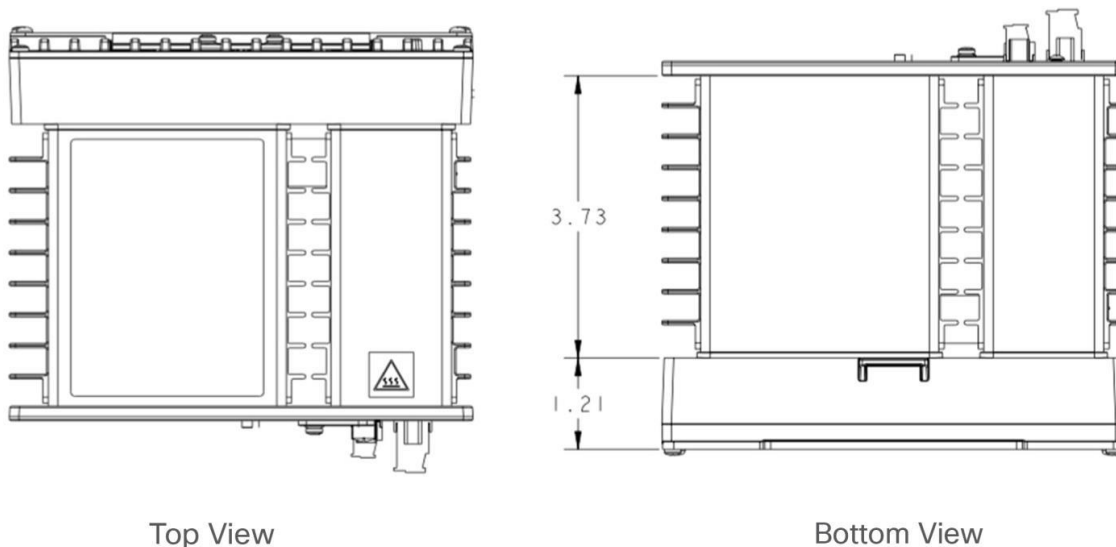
Dimensiones mecánicas del switch IE4000 (vista superior e inferior) [59]
